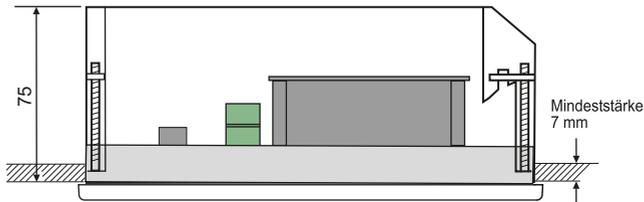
Maßbild MK800-11/MK800-12 mit Blendrahmen BR800 und Unterputzgehäuse UP800. Maßangaben in mm. Beispiel: Hohlwandmontage
